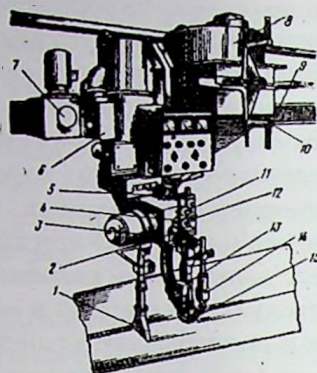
Автомат для электродуговой сварки:
